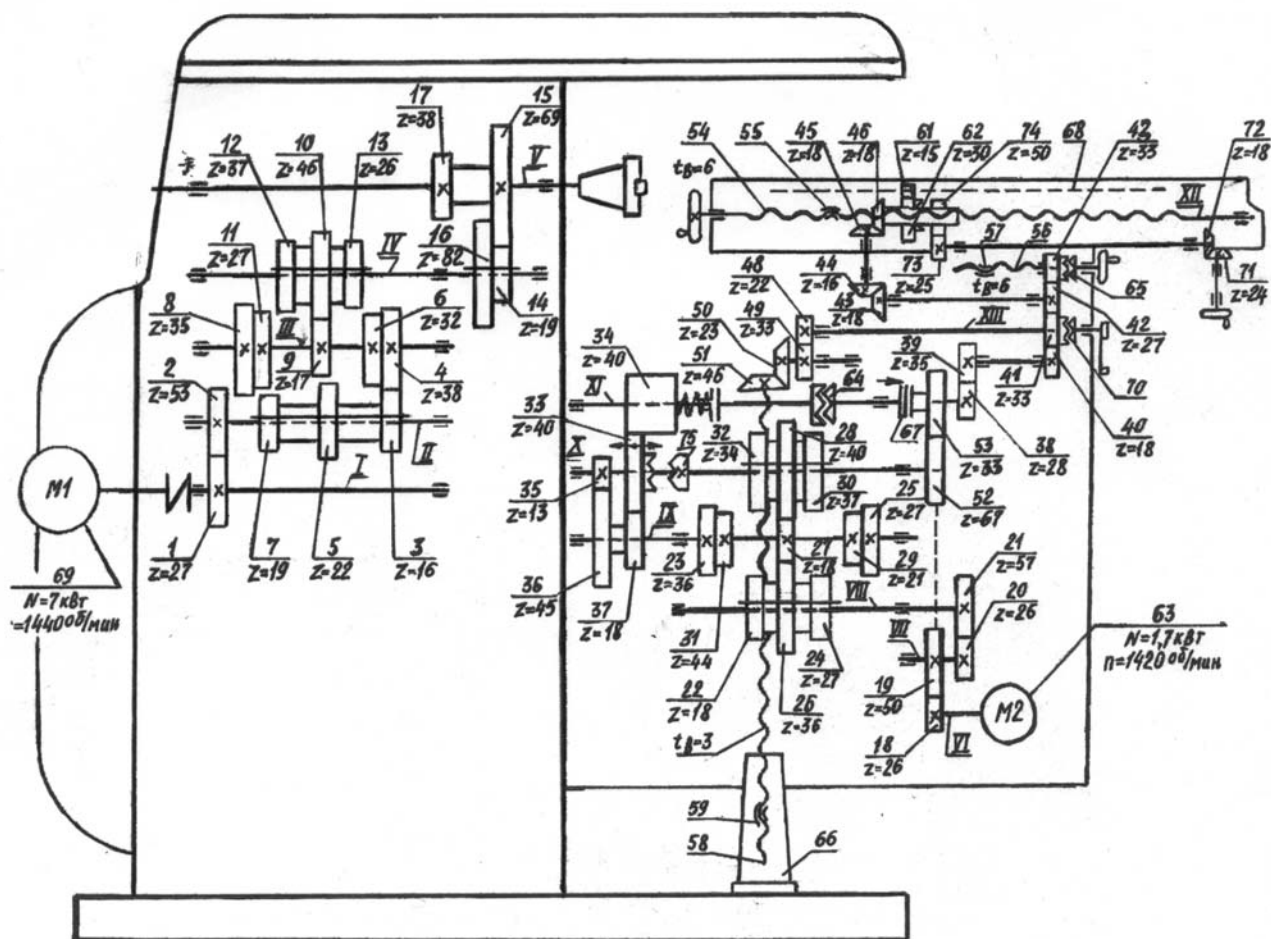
Кинематическая схема универсального горизонтально-фрезерного станка 6М82
